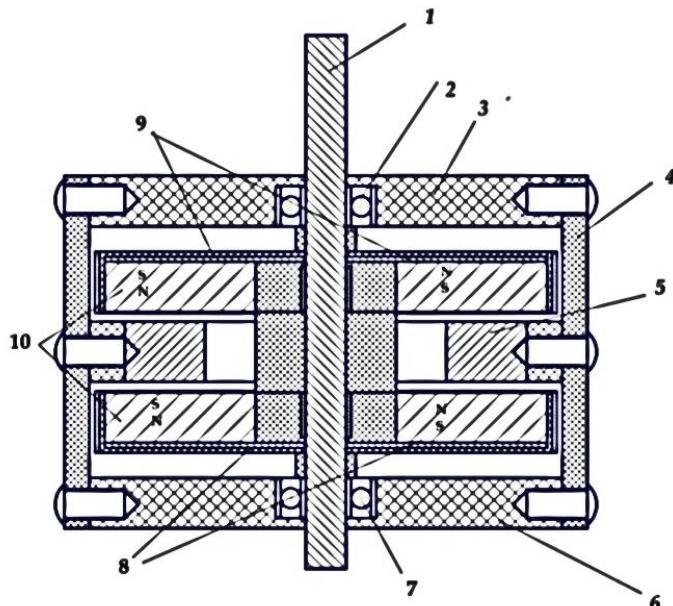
Разрез гибридного электродвигателя второго варианта (1 – вал; 2 – крышка передняя; 3 – корпус; 4 – статор; 5 – крышка задняя; 6 – подшипник; 7 – диск ротора задний; 8 – диск ротора передний; 9 – магниты)
